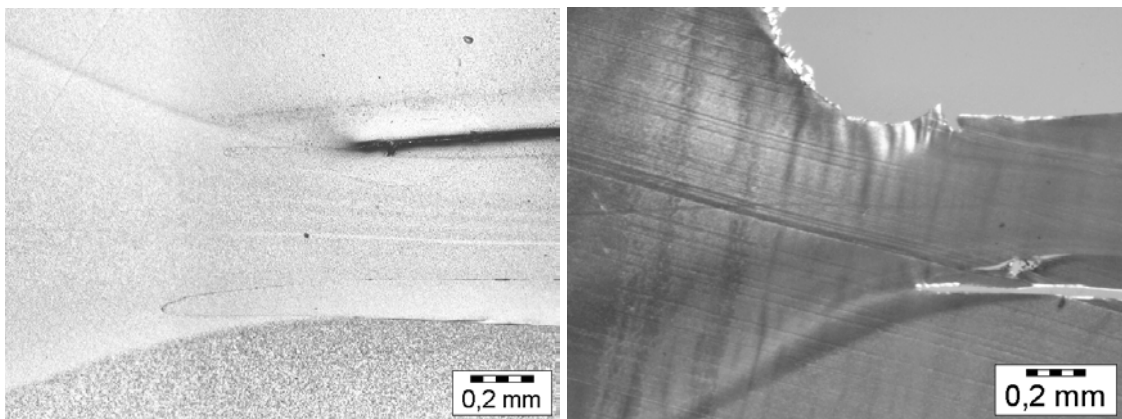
Schweißnahtserie S2, stereomikroskopische Aufnahmen
